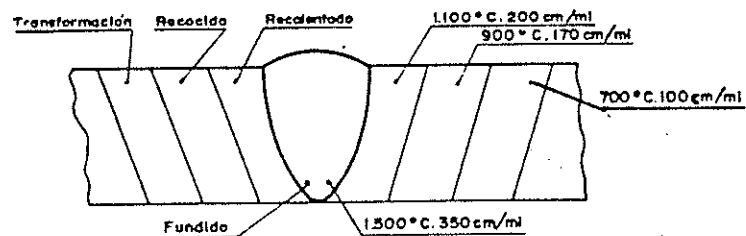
Transformación del metal base durante la soldadura.
